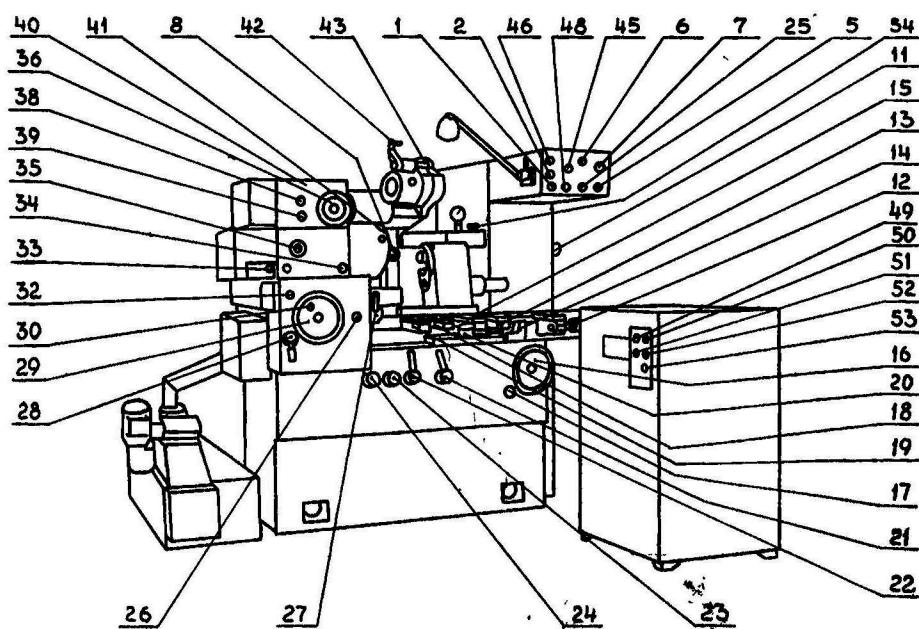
Общий вид станка модели ЗК225А с обозначением органов управления и наялки
